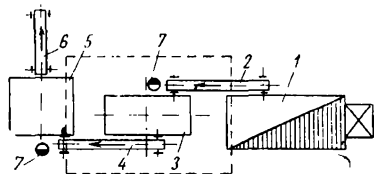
Схема расположения пластинчатых транспортеров в агрегате штамповочного молота: 1 — нагревательная печь; 2 — пластинчатый транспортер; 3 — штамповочный молот; 4 — пластинчатый транспортер; 5 — обрезной пресс; 6 — пластинчатый транспортер; 7 — рабочие места
